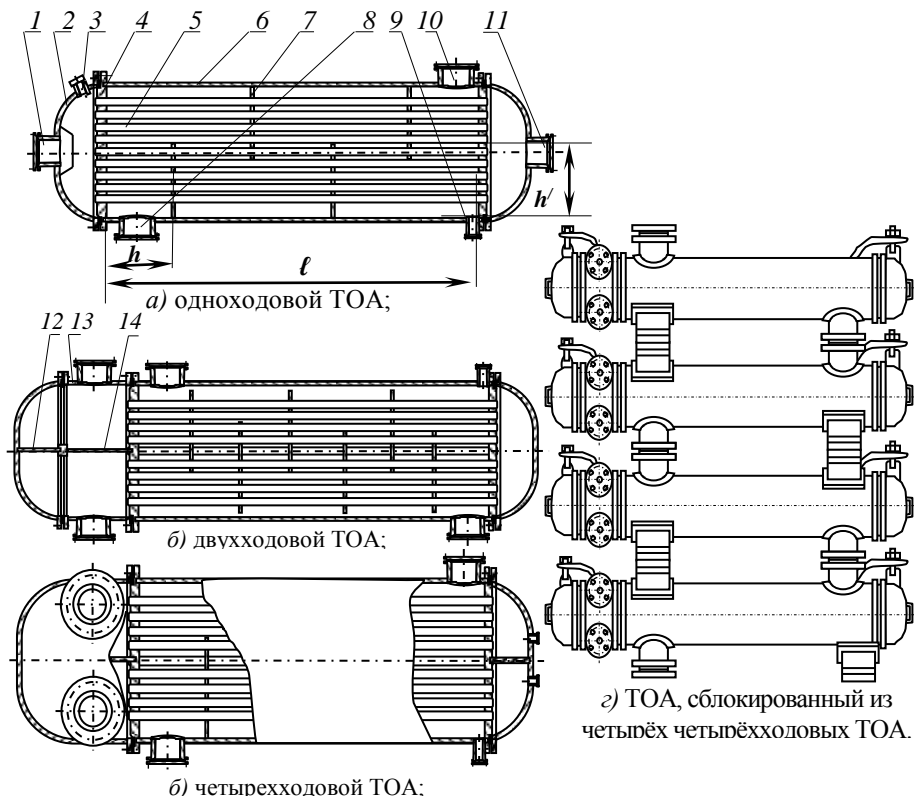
Примеры исполнения кожухо-трубчатых ТОА
